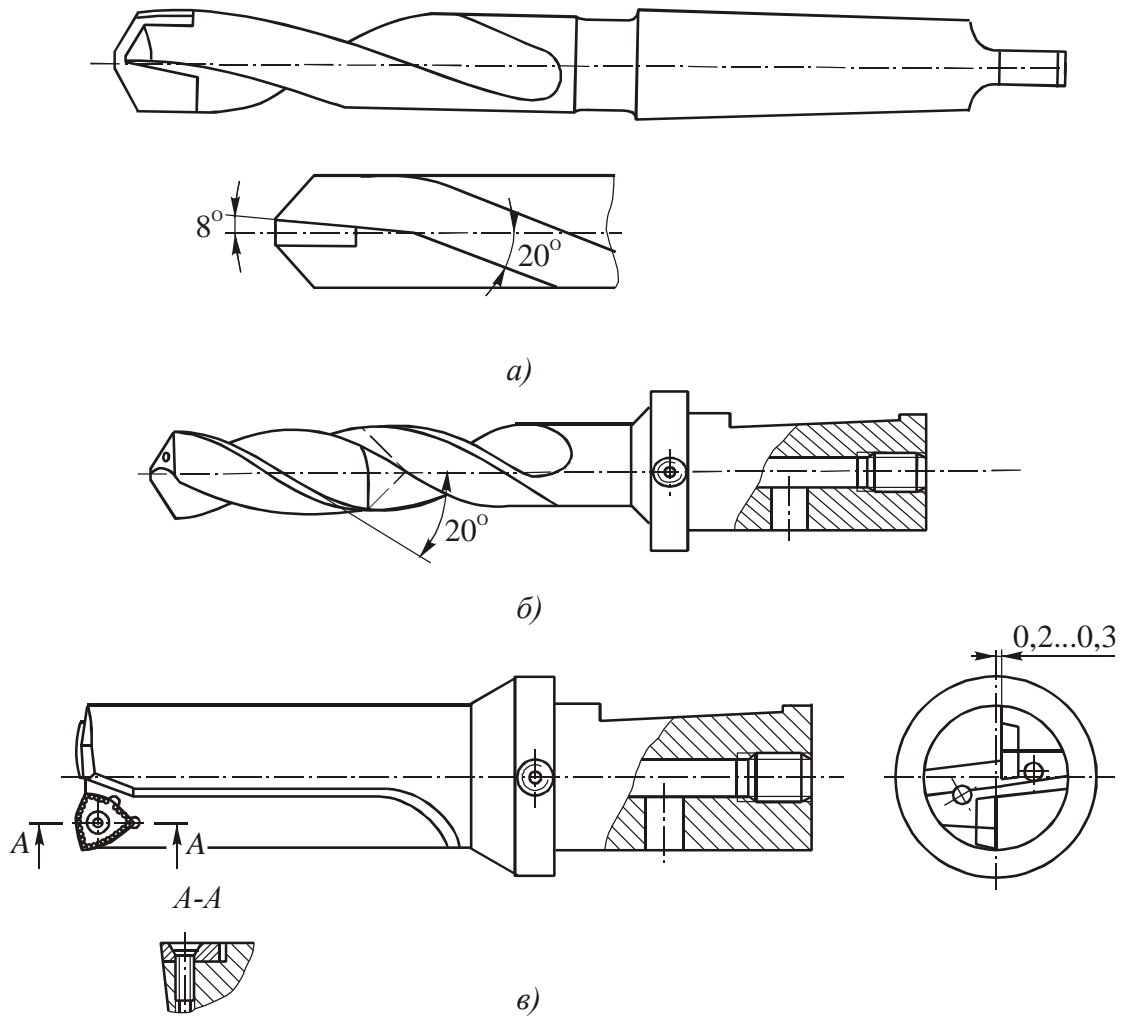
Конструкции твердосплавных спиральных сверл: *а* – с напайной пластиной; *б* – с напайной коронкой; *в* – с механическим креплением СМП
